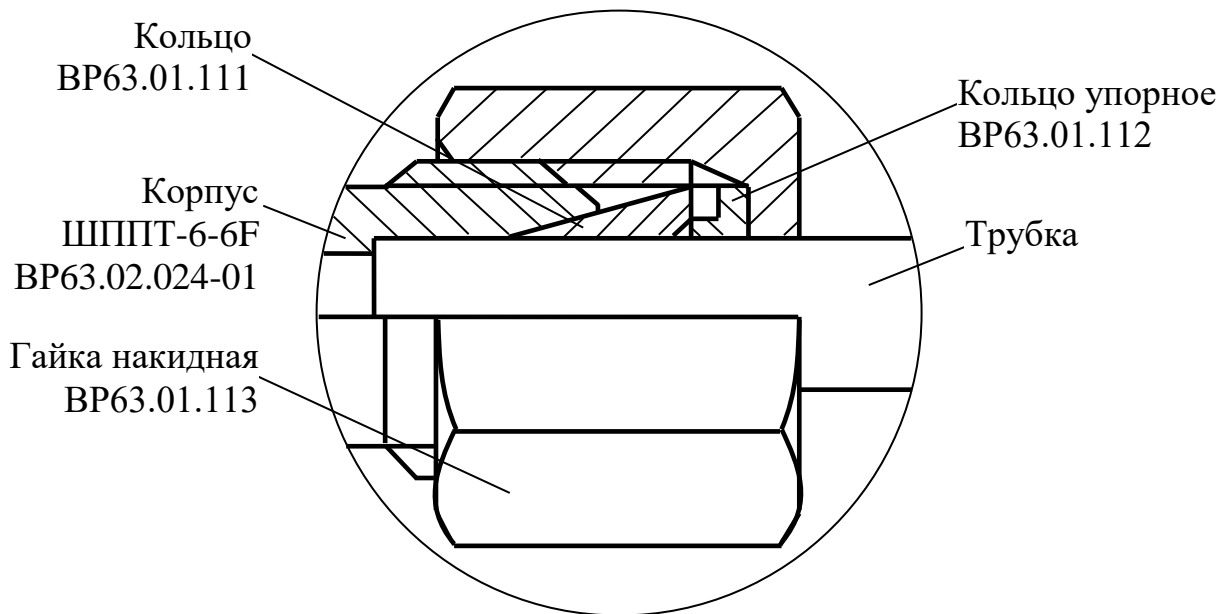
Установка трубки в штуцер подачи пробы
